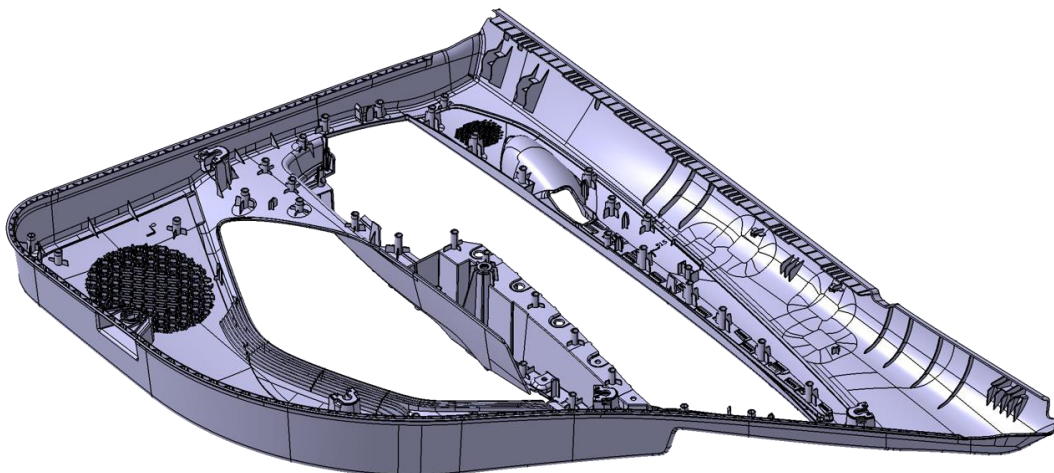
Exemplo de peça para o desenvolvimento de molde da SF Moldes
